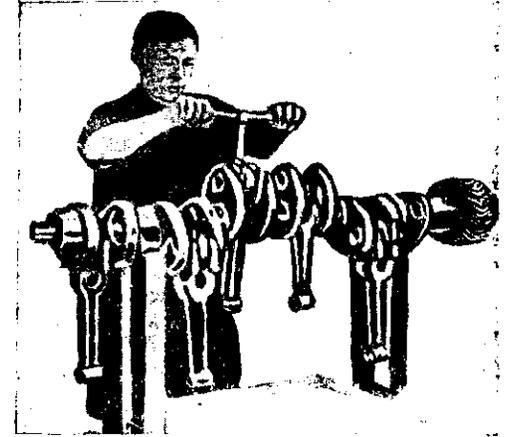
Процесс сборки шатунов на коленчатом вале.
